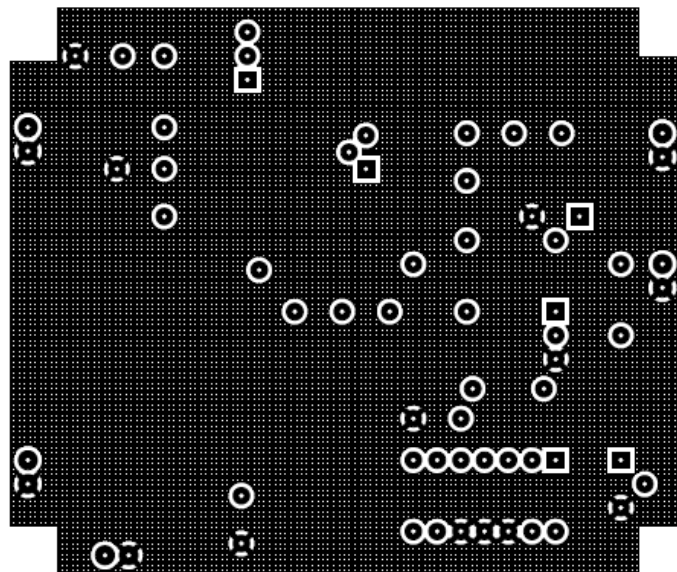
Fotolito capa "BOTTOM" de la PCB.
